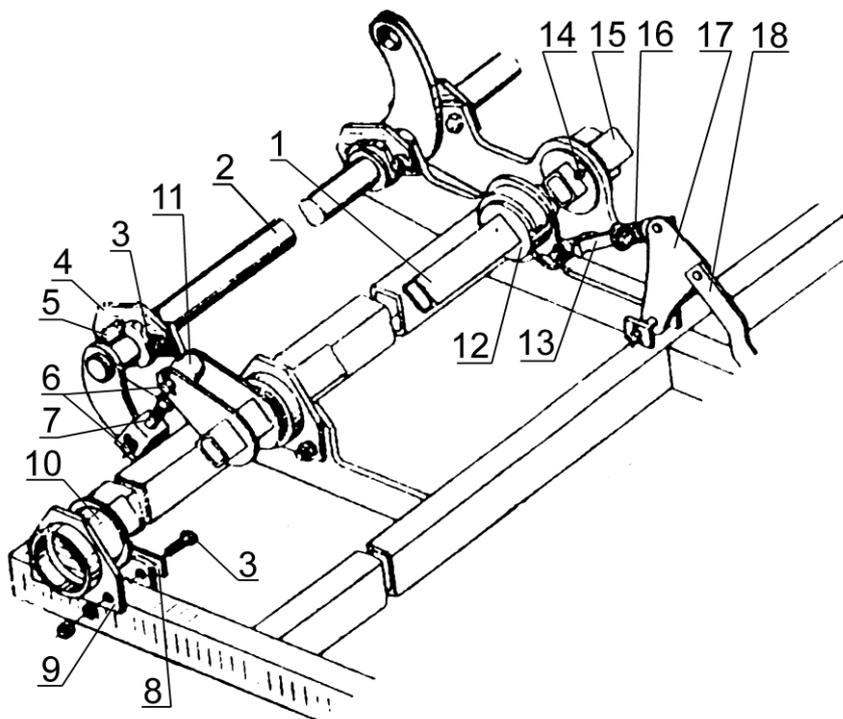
Вал подъема сошников (регулировка винтовой стяжкой) сеялок СЗ-3,6 и СЗП-3,6: 1 - вал левый; 2 - вал передний круглый; 3 - болт; 4 - накладка; 5 - вкладыш; 6 - штырь; 7 - винт регулировочный; 8 - планка; 9 - кронштейн; 10 - вкладыш; 11 - кулиса; 12 - кривошип; 13 - тяга; 14 - шплинт; 15 - вал правый; 16 - пружина; 17 - кулиса; 18 - тяга
